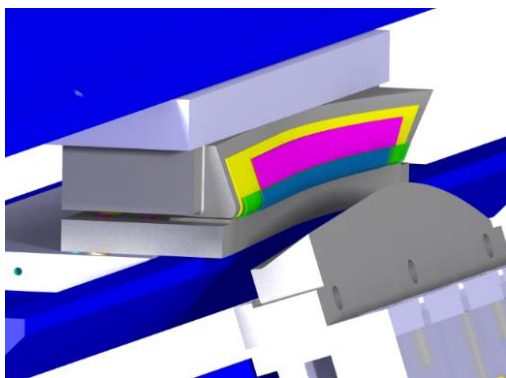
Skalierbare Demonstratoren in einem Werkzeugsatz
